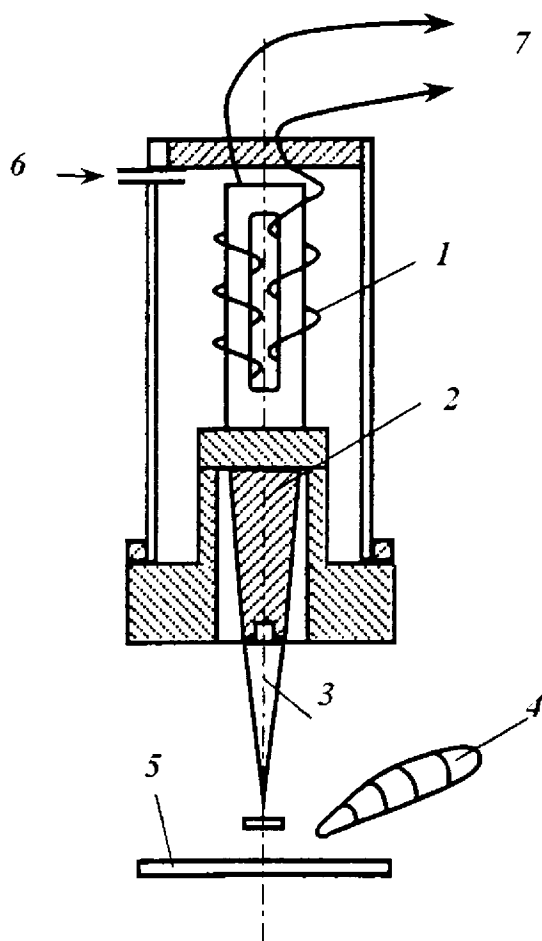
Схема ультразвуковой обработки: 1 – магнитоstrictionный вибратор; 2 – концентратор; 3 – инструмент; 4 – сопло для подачи абразивной суспензии; 5 – деталь; 6 – вода для охлаждения вибратора; 7 – выходные концы обмотки вибратора для подключения к генератору высокой частоты
